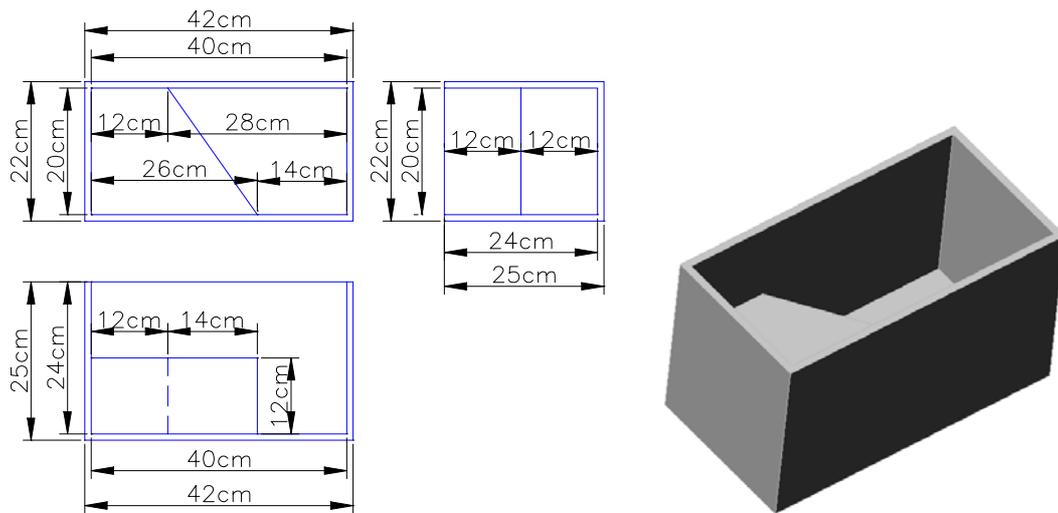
Projeto de construção de caixa para refração de onda mecânica
